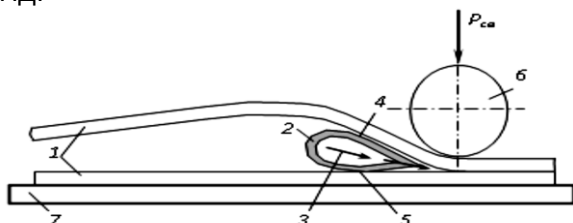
Схема сварки клином нагретым воздухом
